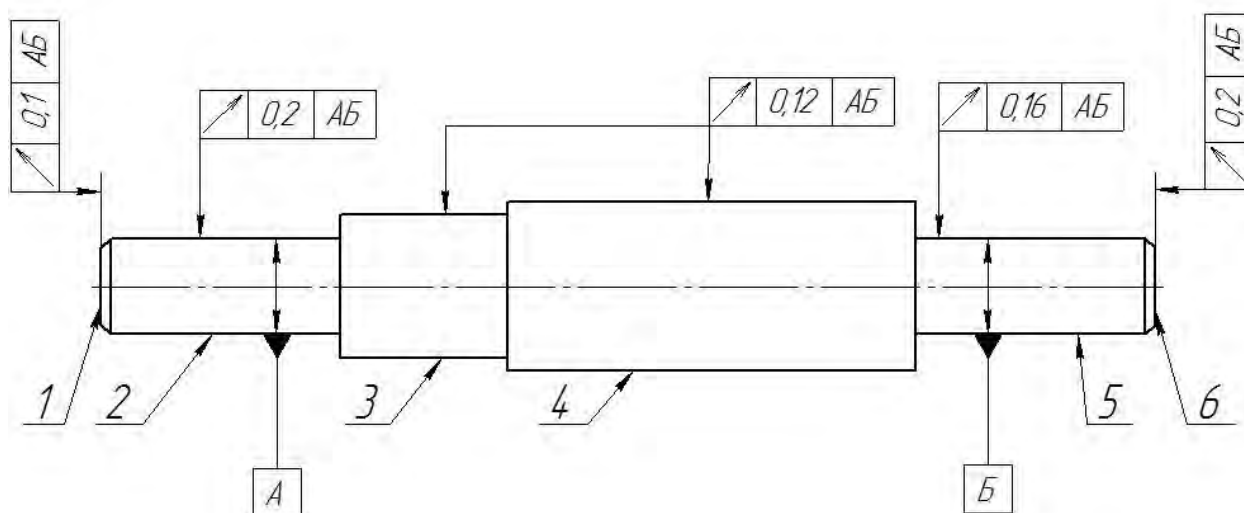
Фрагмент чертежа детали с допусками биения
